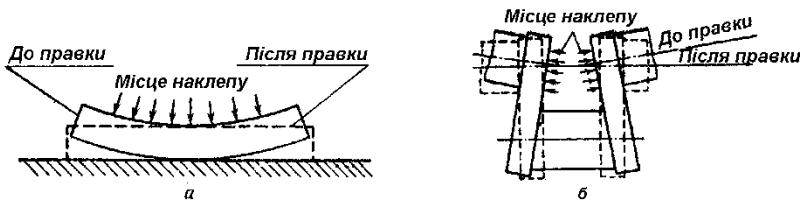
Схема правки наклепом: а – бруска; б – колінчастого вала
